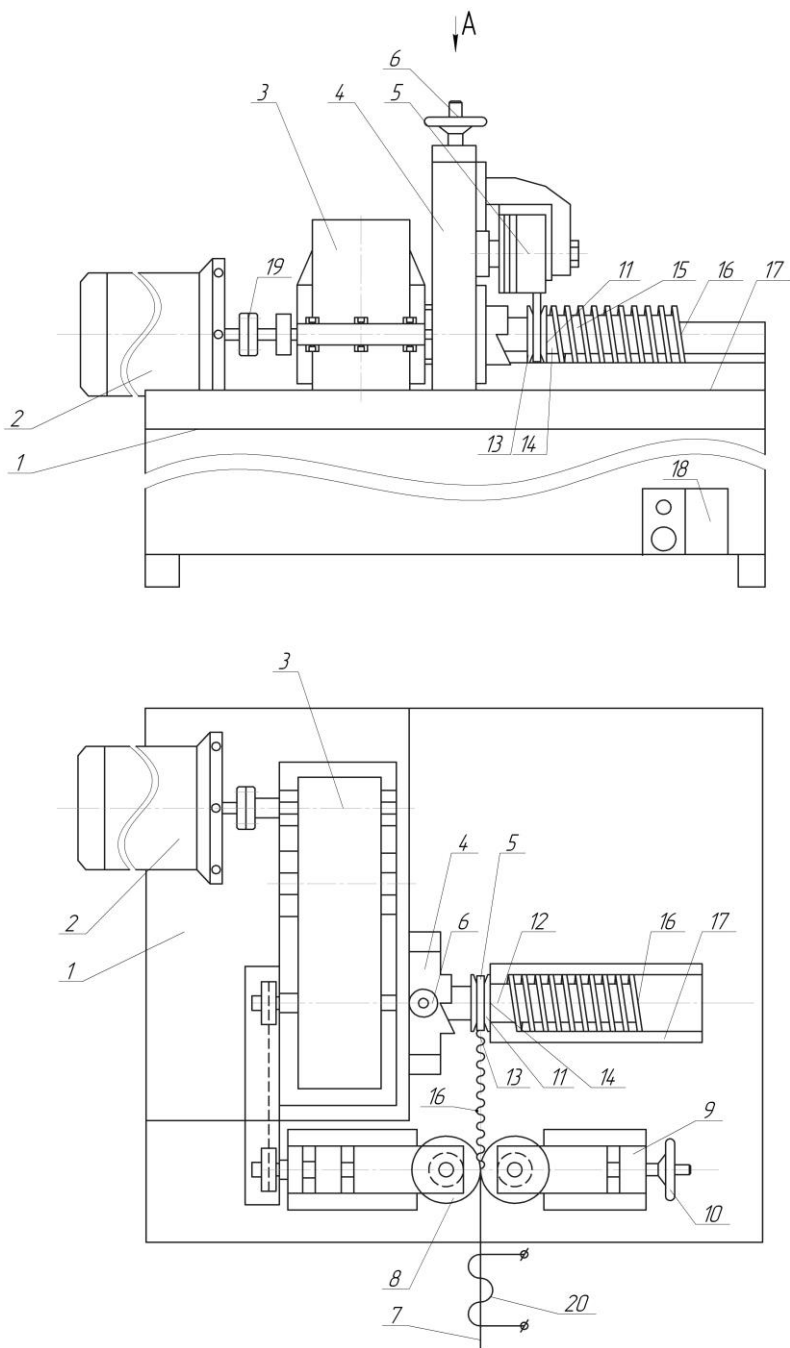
Пристрій для виготовлення гвинтових гофрованих заготовок з різним профілем гофр
